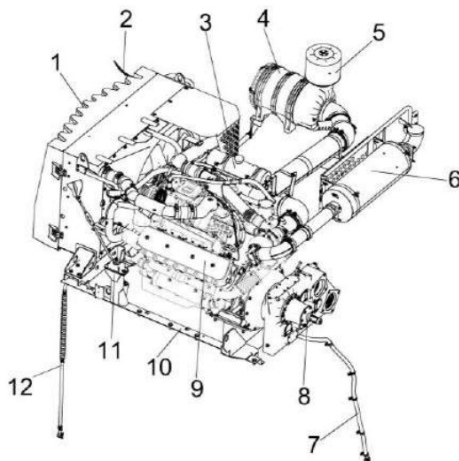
Установка двигателя: 1 – радиатор; 2 – цепочка ограничительная; 3 – бачок расширительный; 4 – фильтр воздушный; 5 – воздухозаборник вращающийся; 6 – глушитель; 7 – сливной рукав масла из картера двигателя; 8 – мультипликатор; 9 – двигатель; 10 – рама подмоторная; 11 – амортизатор; 12 – сливной рукав охлаждающей жидкости
